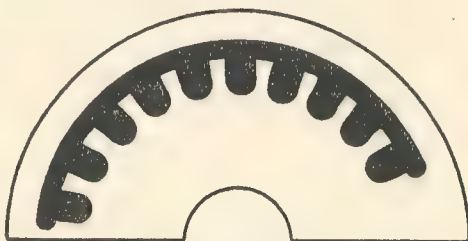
Die halbkreisförmige Scheibe mit der ausgefüllten Zeichnung.
